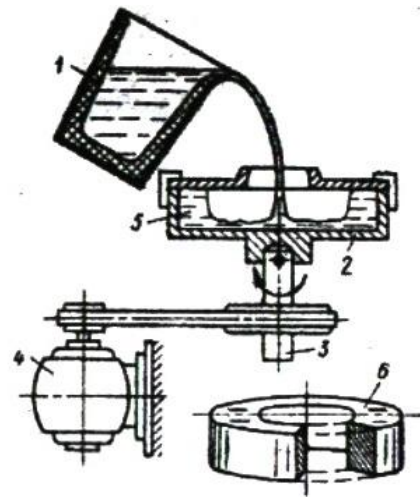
Схема получения отливки при вращении формы вокруг вертикальной оси: 1- расплав, 2- форма, 3- шпиндель, 4- электродвигатель, 5- расплав, 6- отливка
